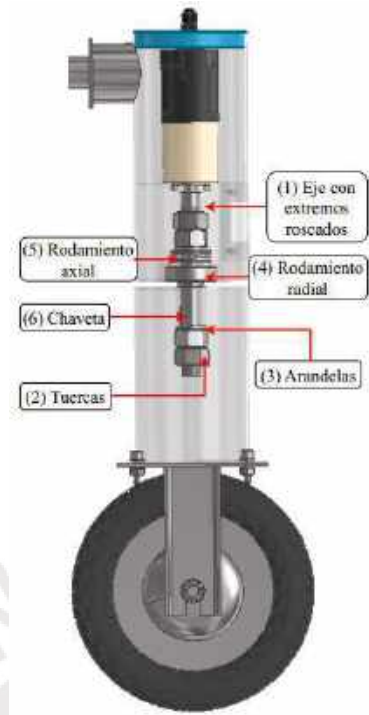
Componentes del acople del motor a pasos con la rueda motorizada.
